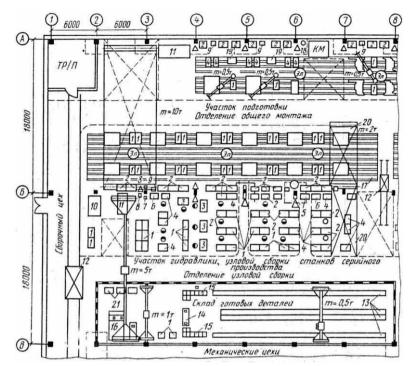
Планировка оборудования и рабочих мест сборочного цеха шлифовальных станков [1]
